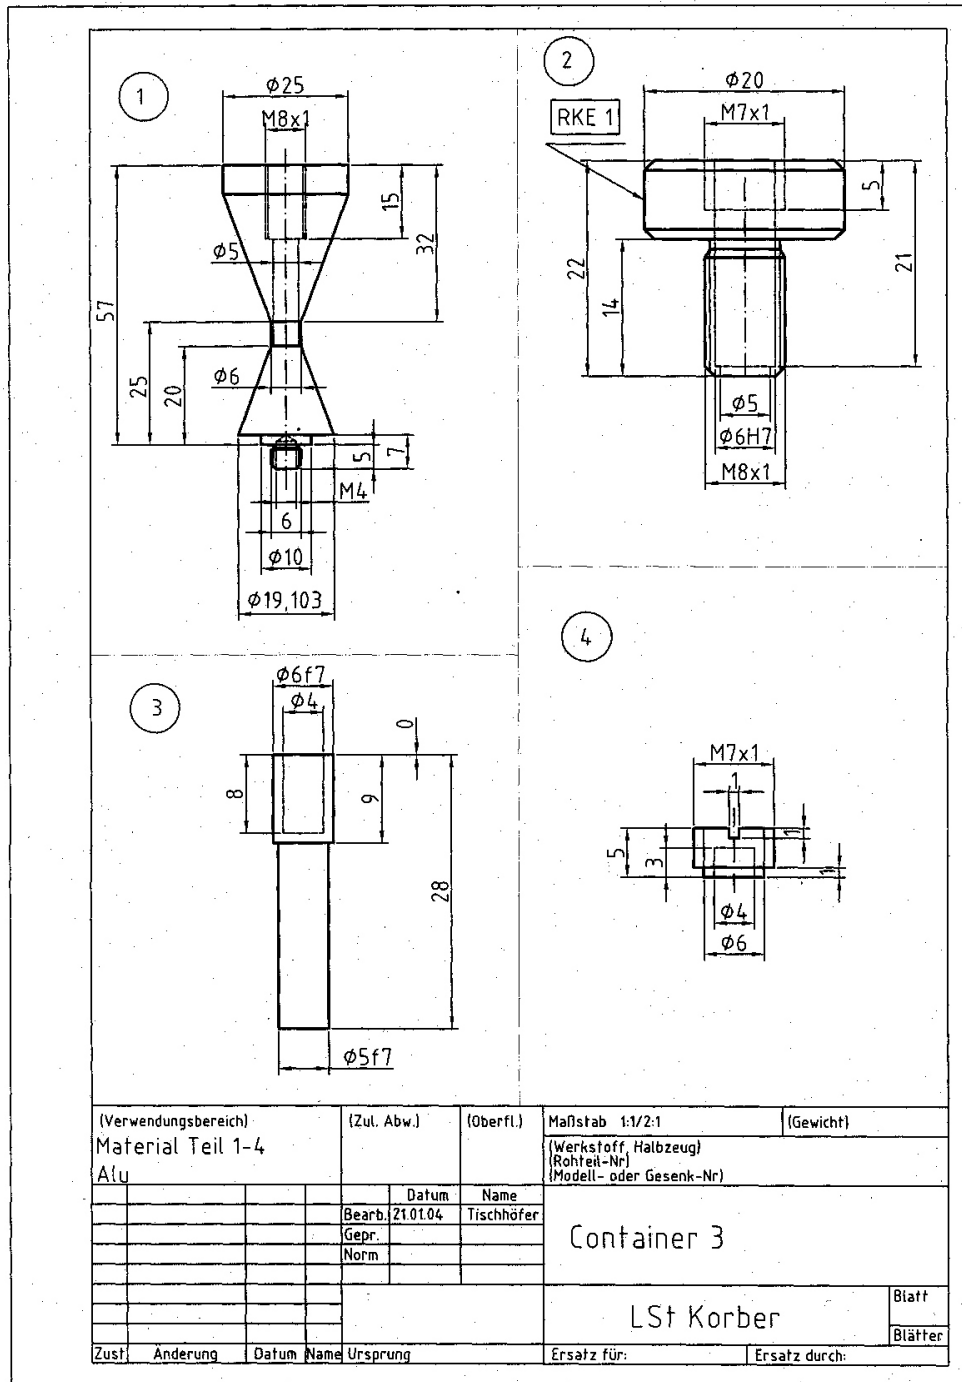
Die technische Skizze der vier Vanadiumbauteile des Probencontainers.
